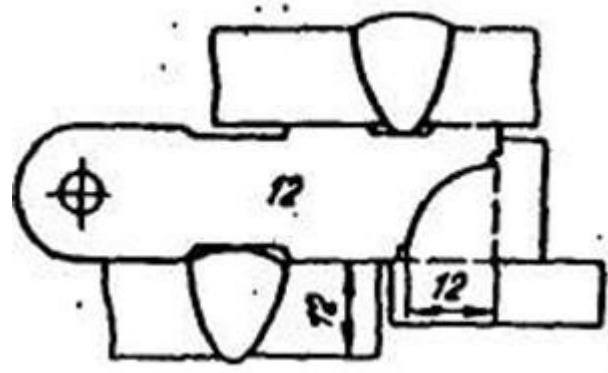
Специальный шаблон для контроля сварных швов.
